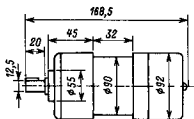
13 Габаритные и установочные размеры двигателя типа ДВ75
